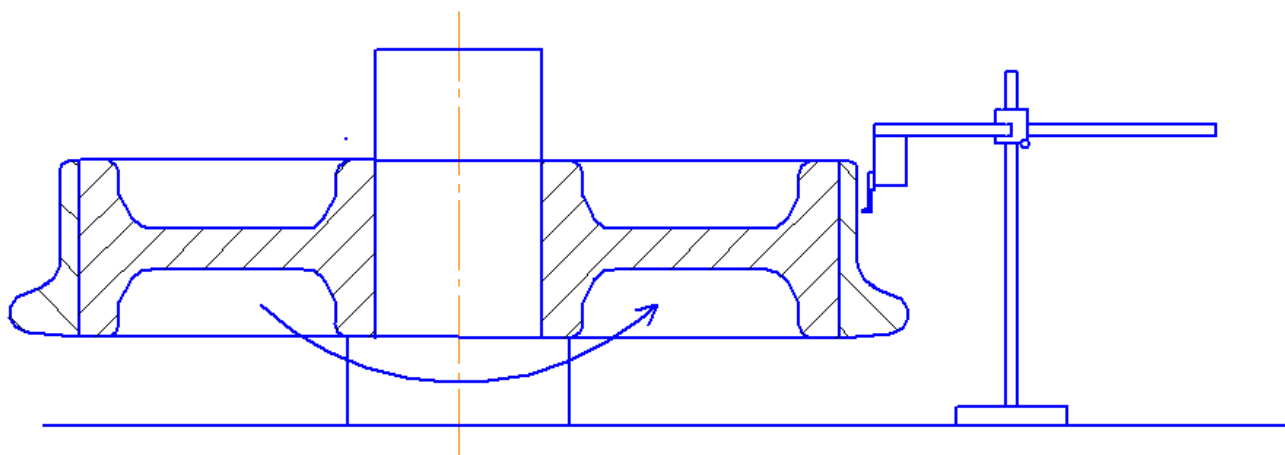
Схема станда для измерения шероховатости на колесе
